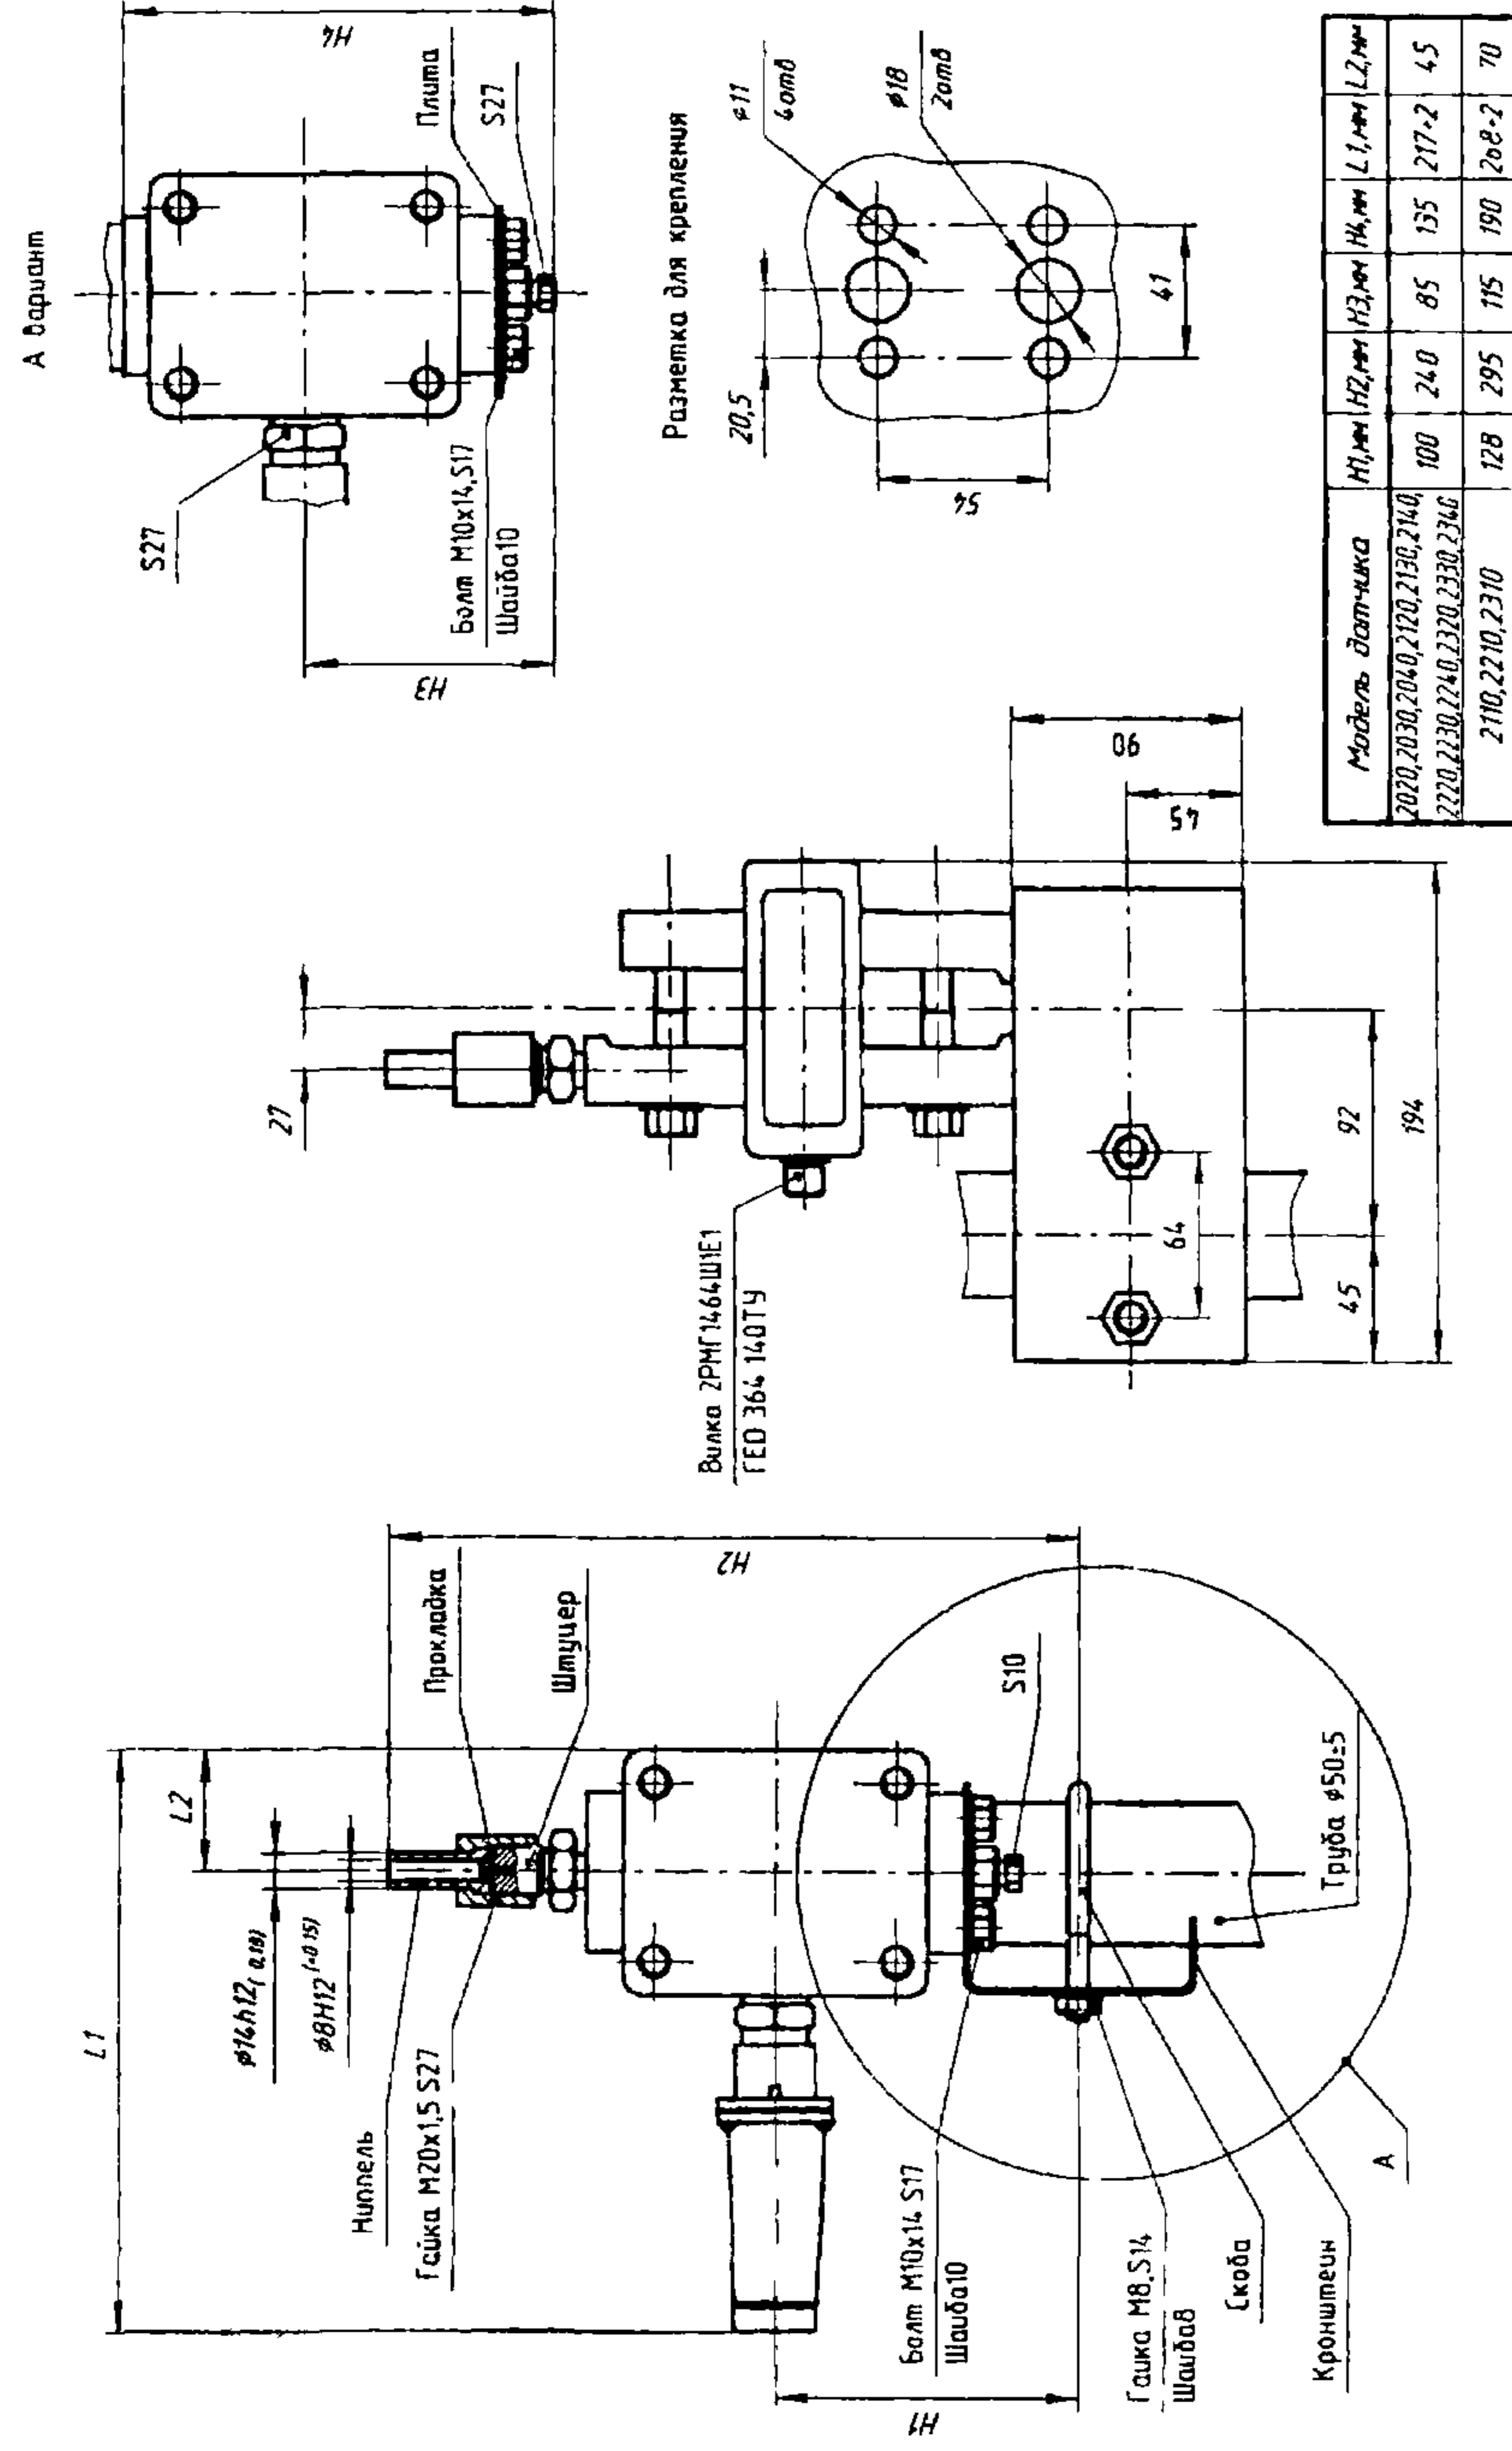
Установочные и присоединительные размеры датчиков модели 2020, 2030, 2040, 2110, 2120, 2130, 2140, 2210, 2220, 2230, 2240, 2310, 2320, 2330, 2340 с установленными ниппелями под накидные гайки
